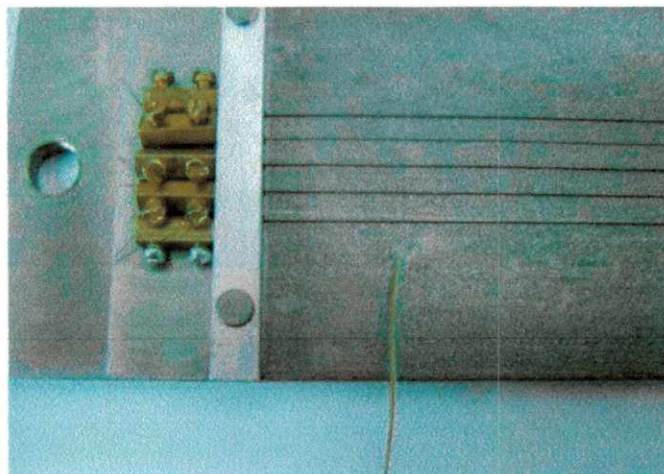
Microtermopar tipo K soldado no molde.
